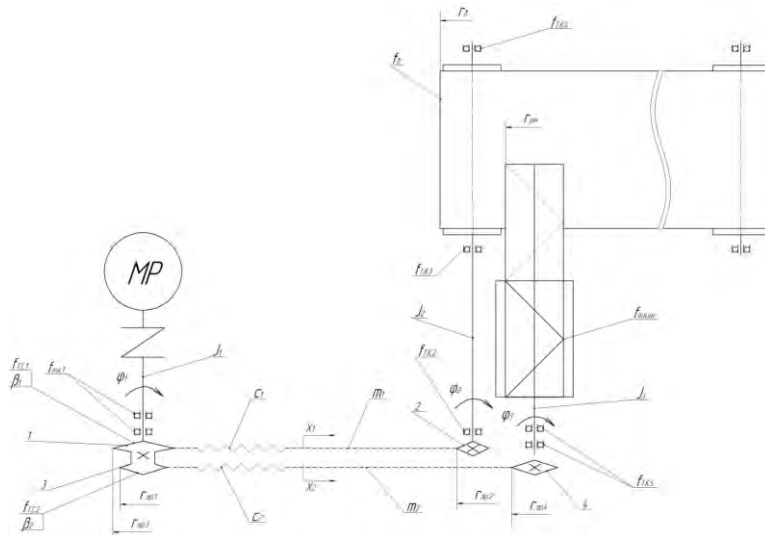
Розрахункова схема приводу конвеєра-дозатора
